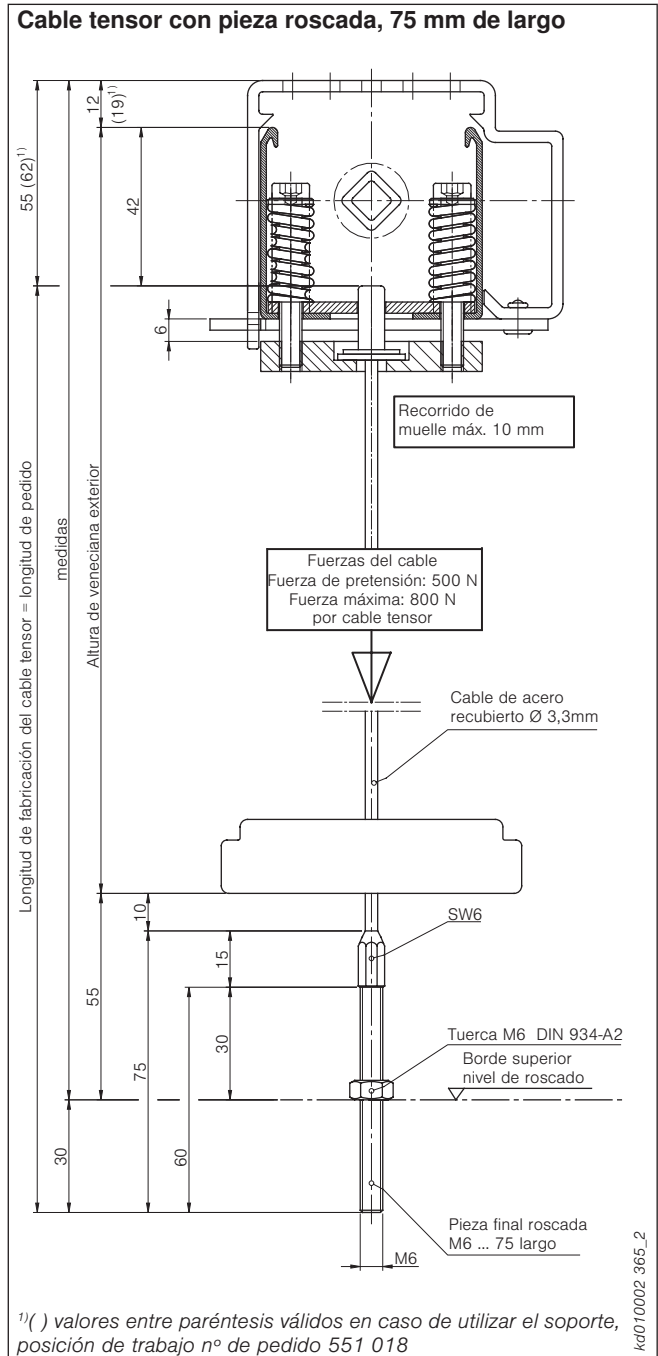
Cable tensor con pieza final roscada, 75 mm de largo
